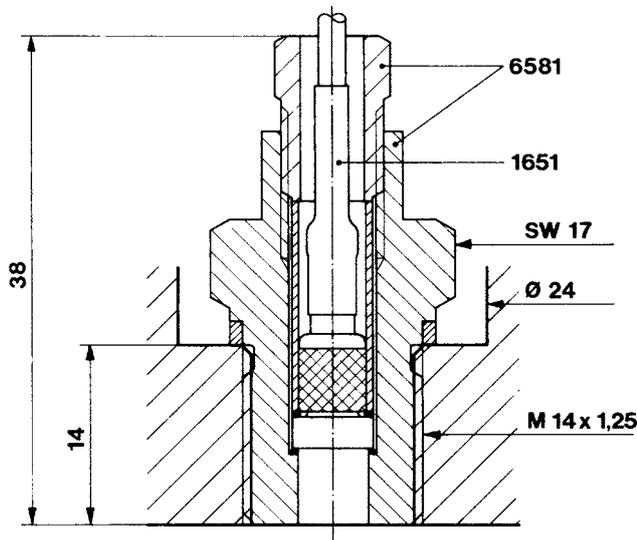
Einbau mit Kunststoff-Montageadapter Typ 6581
